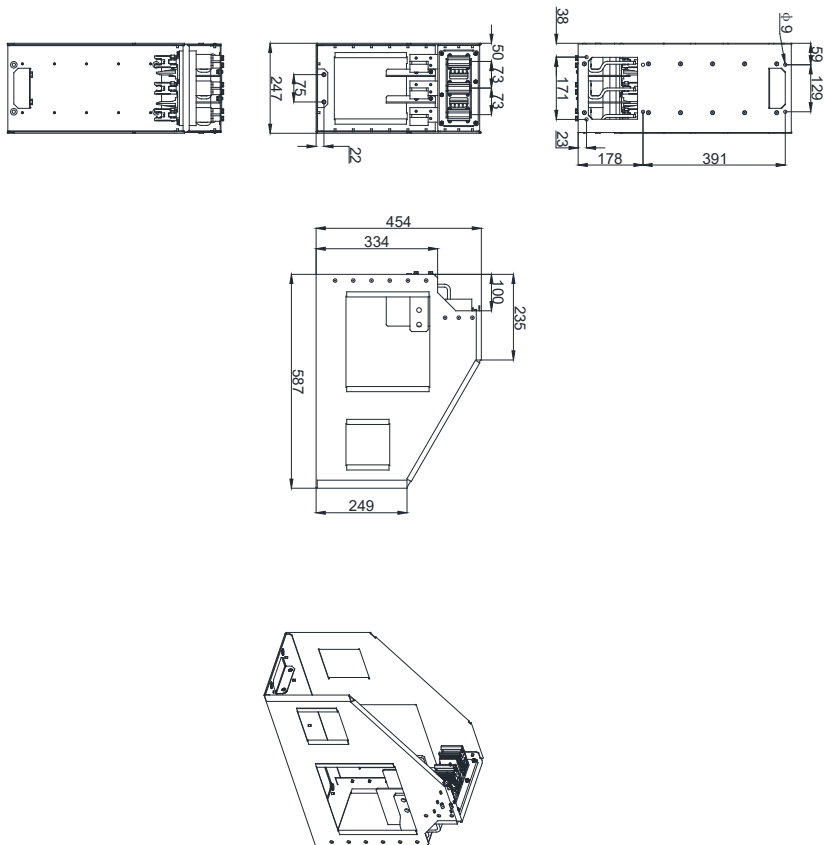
Размеры комплекта для быстрой установки N8-quick-kit
